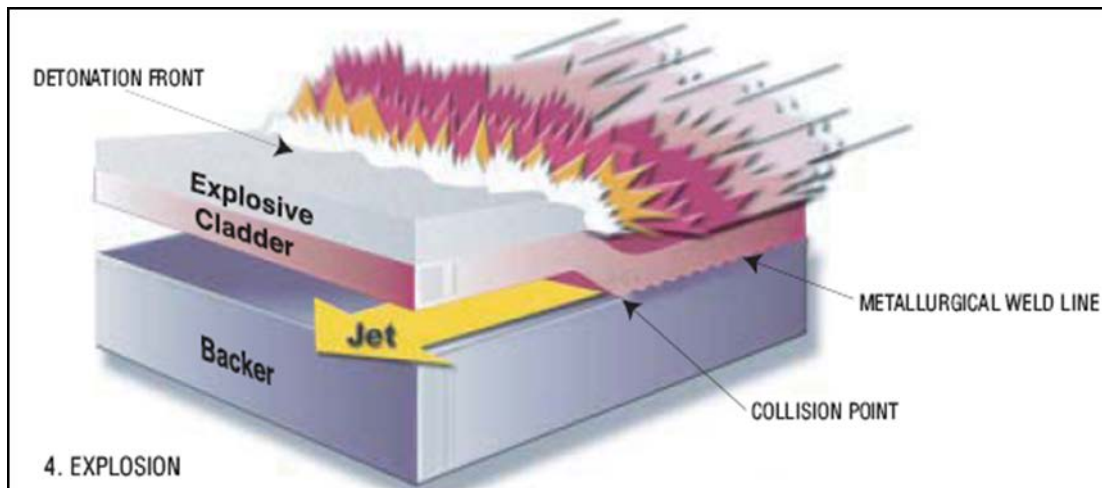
Schematische Darstellung der Prozesstechnik beim Explosions-schweißen .
